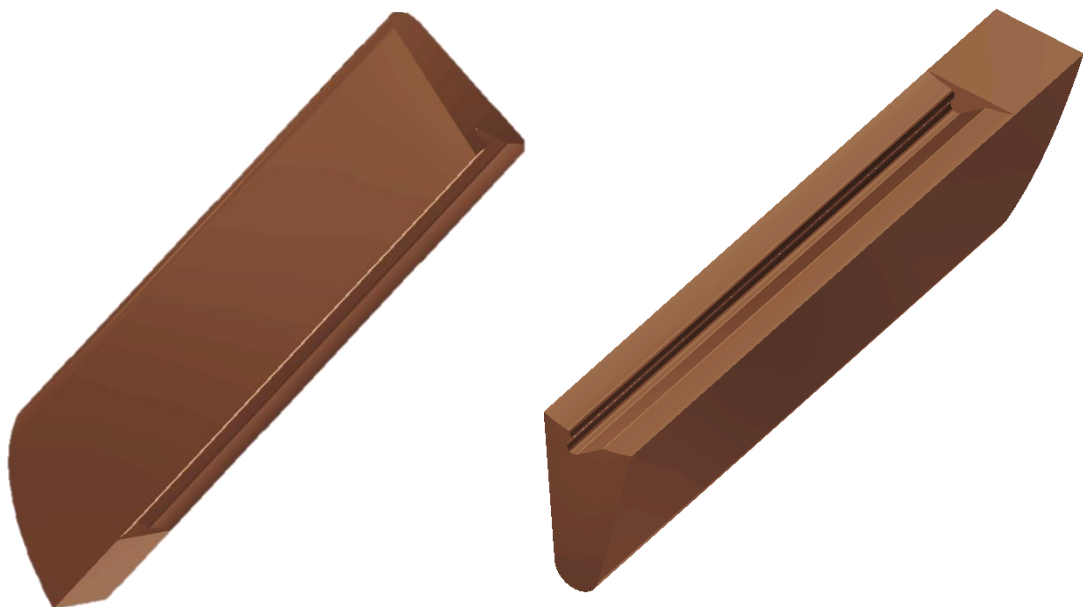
Model hlavice palcátu pro lití do skořepinové formy
